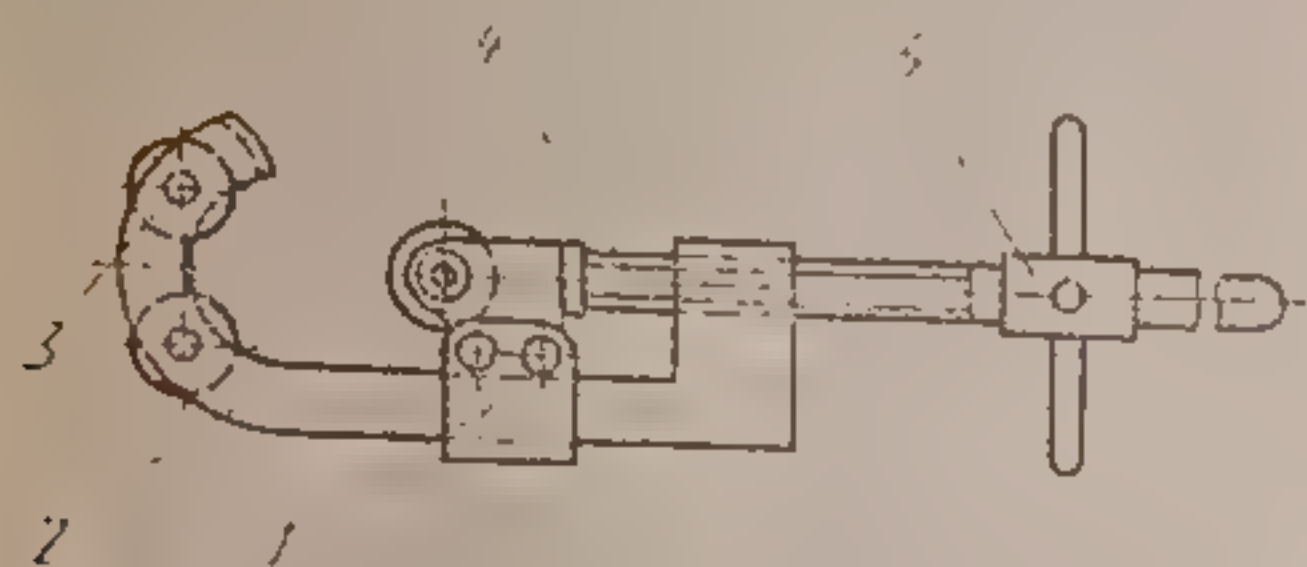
Труборез: 1 — ползун; 2 — корпус; 3 — ролик; 4 — винт; 5 — рукоятка
